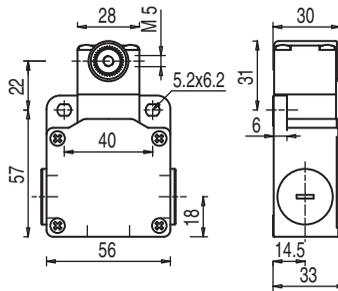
Dimensiones S300-M13C3-M20-CB en mm
